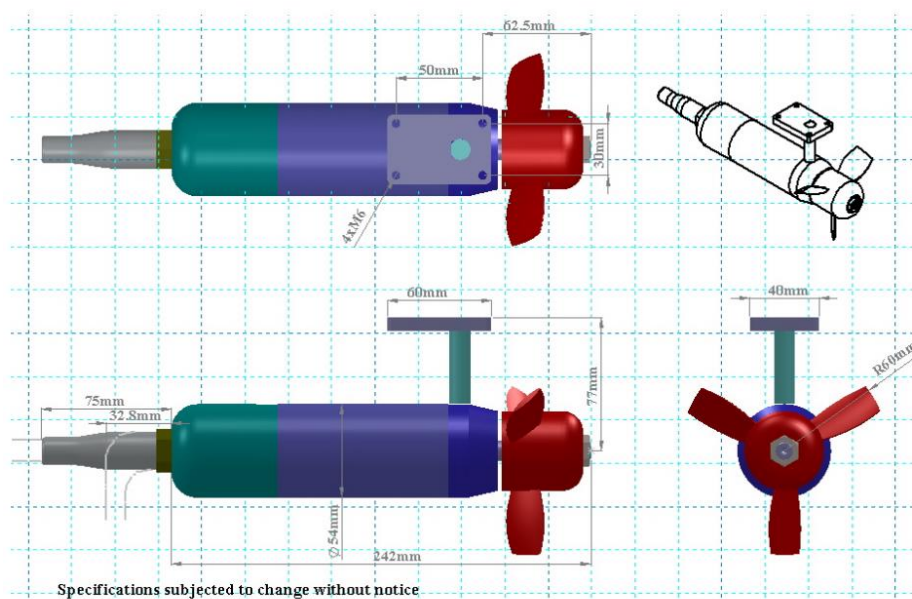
Внешний вид винтомоторного агрегата 049-Е 120-100
